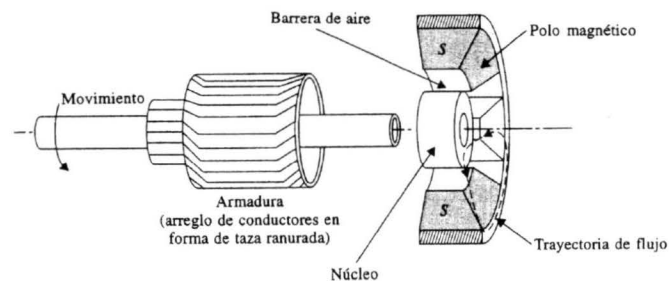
Rotor de una máquina de CD, [Kuo, 1996].
